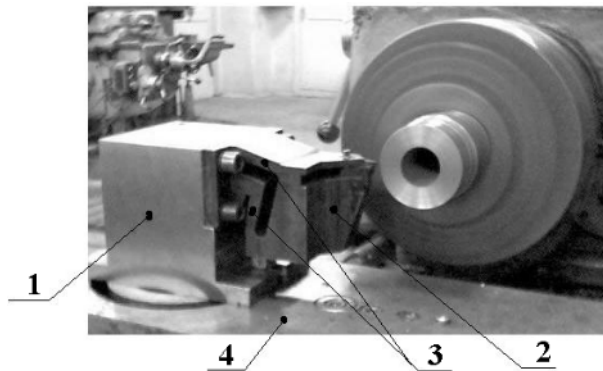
Різцетримач з орієнтованою жорсткістю для підвищення сталості токарної обробки
